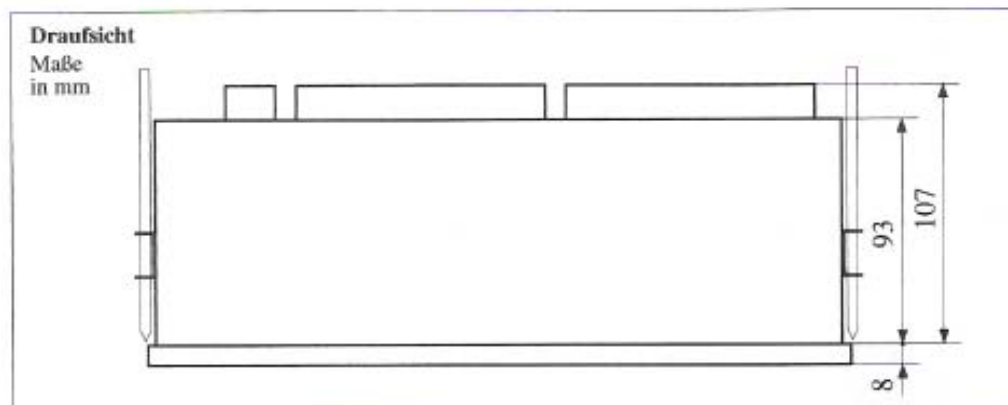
Einbaumaße DAA 288-120/240, Draufsicht
